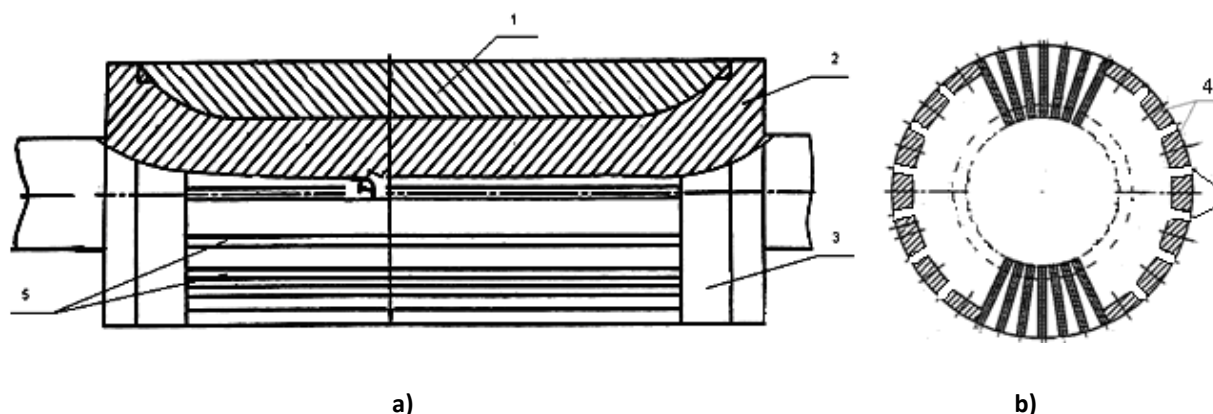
Rotorul motorului sincron cu magneți permanenți: a) fragment de rotor cu bare; b) secțiunea transversală a rotorului: 1 - bară ; 2 - corp rotor ; 3 - inele de scurtcircuit ; 4 - magneți ; 5 - bare din aluminiu
